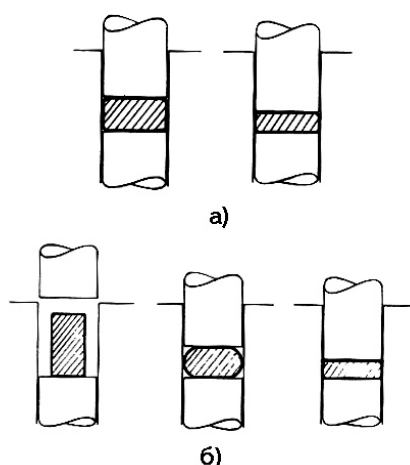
Схемы закрытой штамповки пористых заготовок: а – простой допрессовкой; б – с элементами осадки
